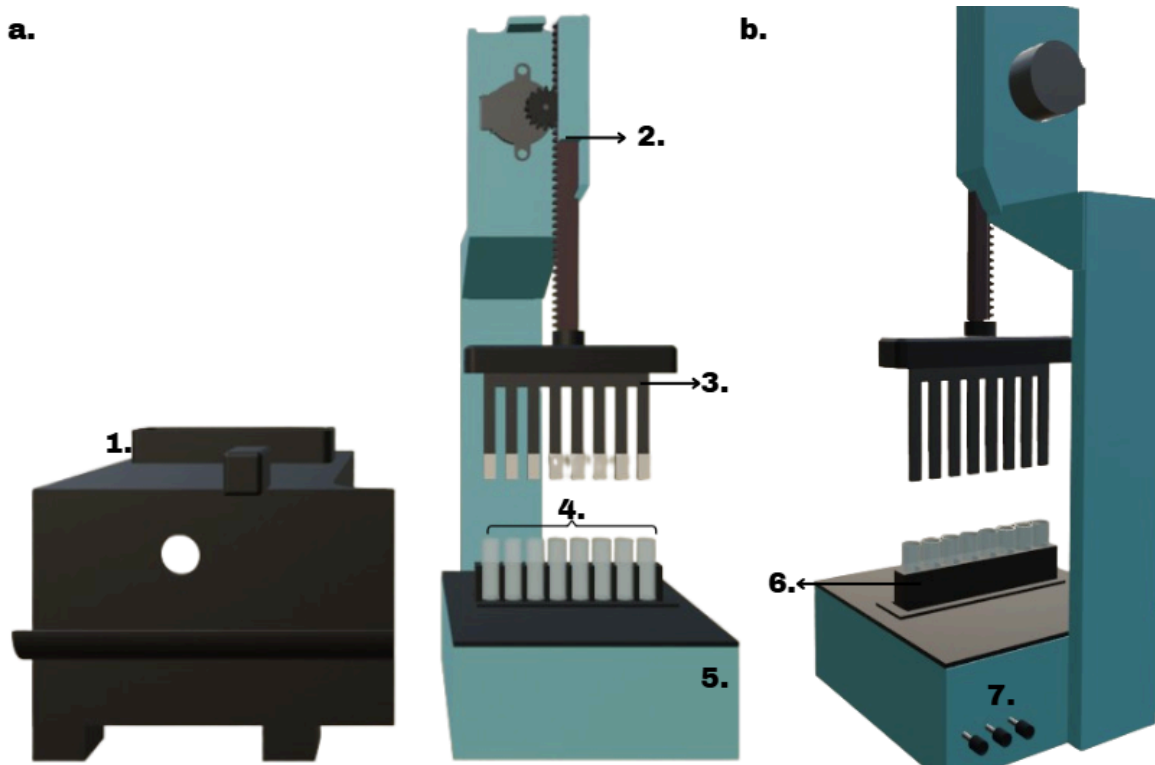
Projeto 3D do sistema de imersão automatizada. (a) Lado frontal; (b) Lado posterior.
